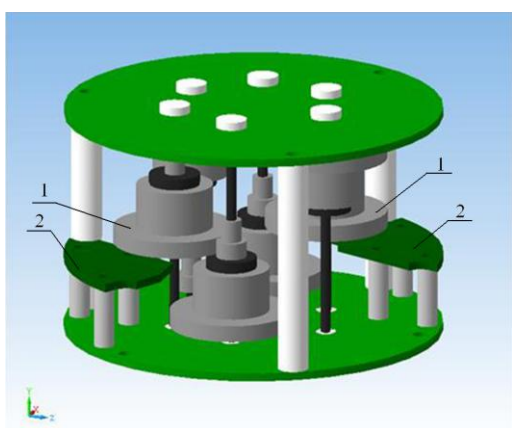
3D-модель датчика поворота вала: 1 – зубчатое колесо с кодом Грея; 2 – печатная плата с ИК-преобразователями.
